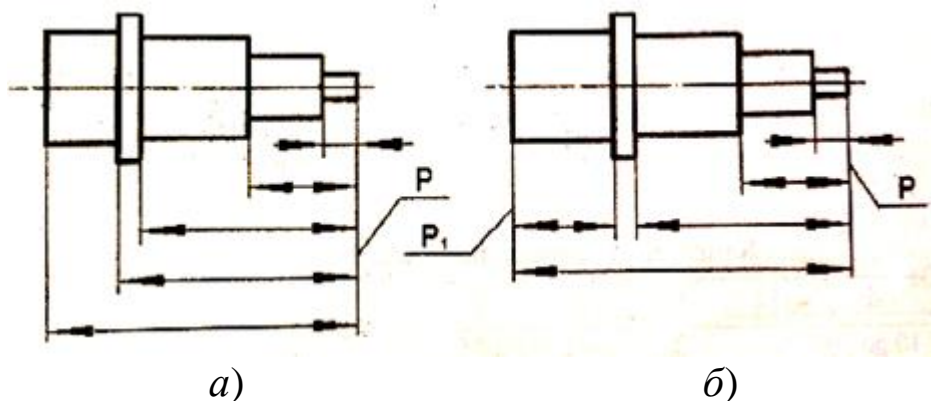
Простановка размеров: а – с одной стороны; б – с главной и вспомогательной базой (Р – база)
